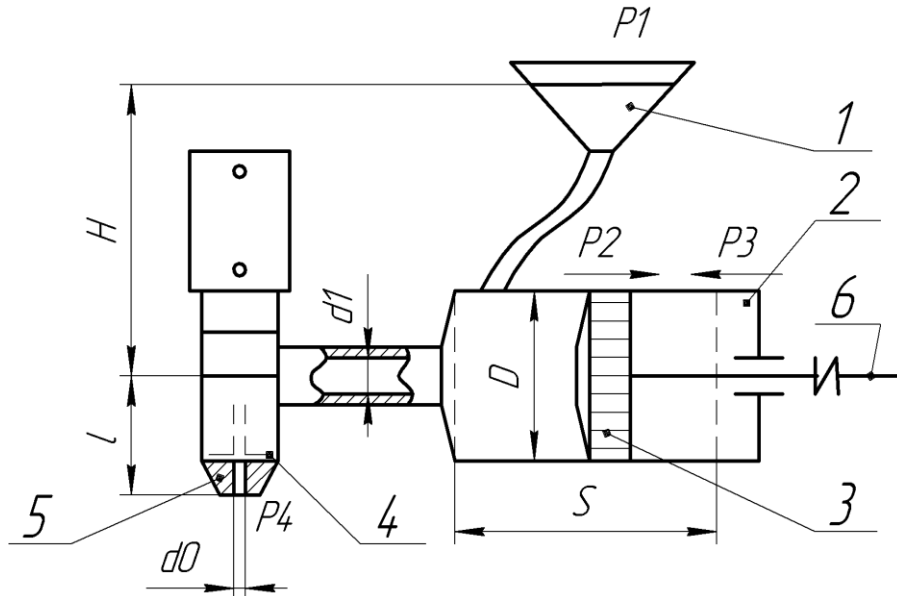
Розрахункова схема поршневого дозатора (ліва частина дозатора)
